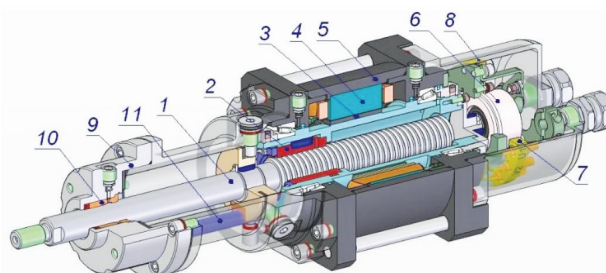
Устройство электроцилиндра 1 — шток; 2 — гайка; 3 — магнит;
